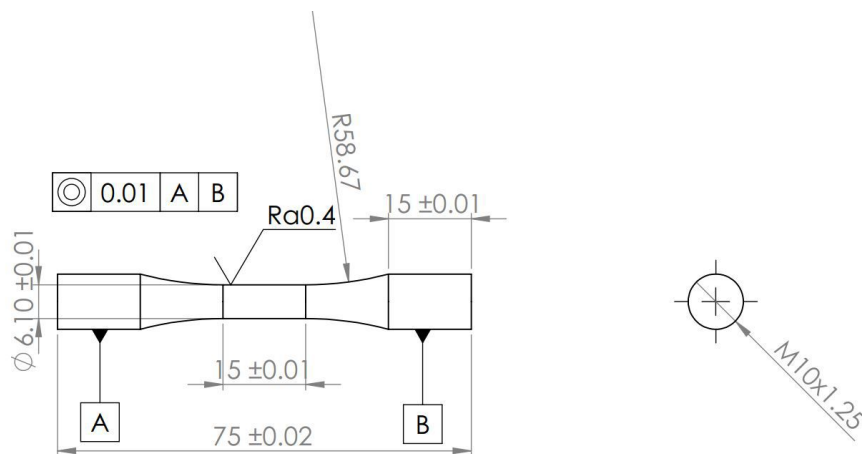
Géométrie d'éprouvettes d'essai d'écrouissage cyclique
